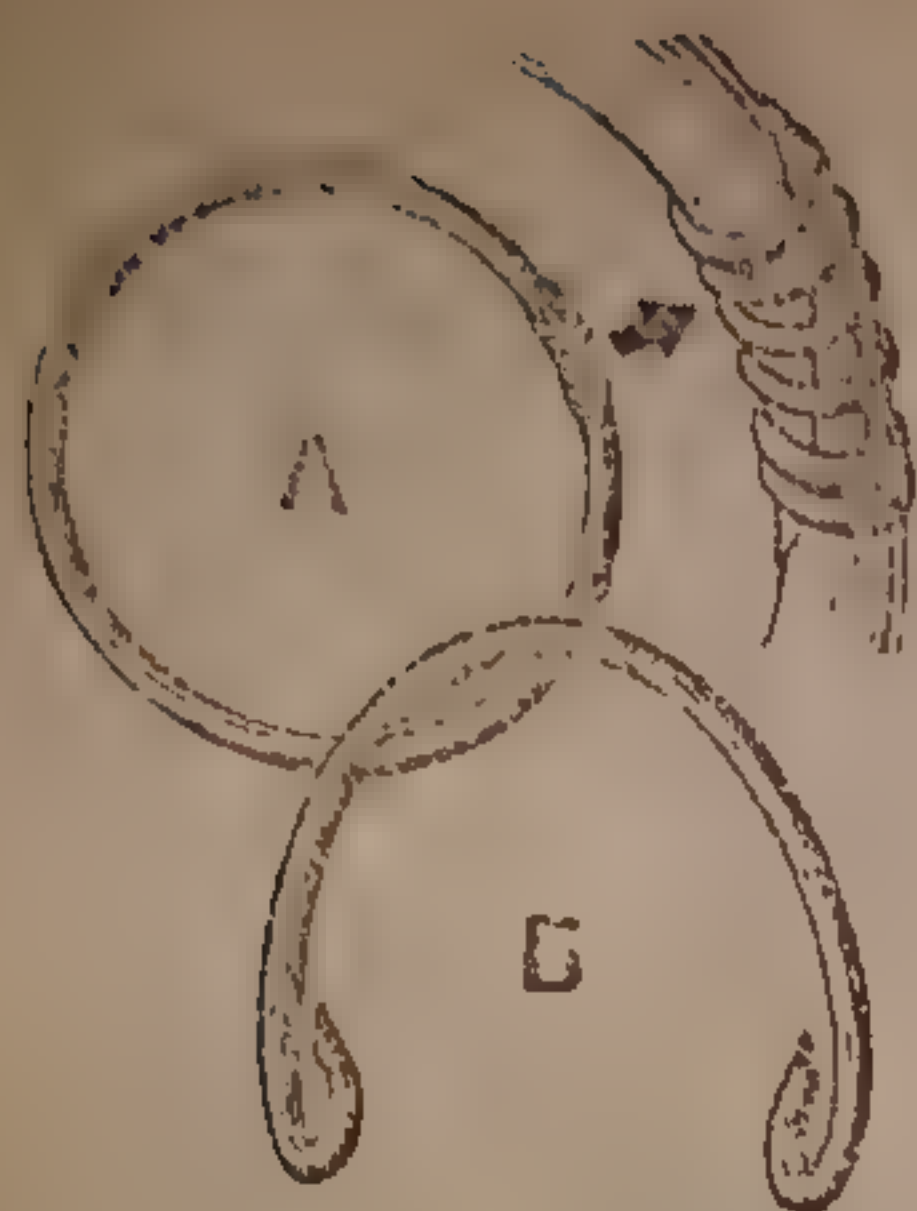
Сращивание концов обруча [А] и заготовка ручки [Б]
